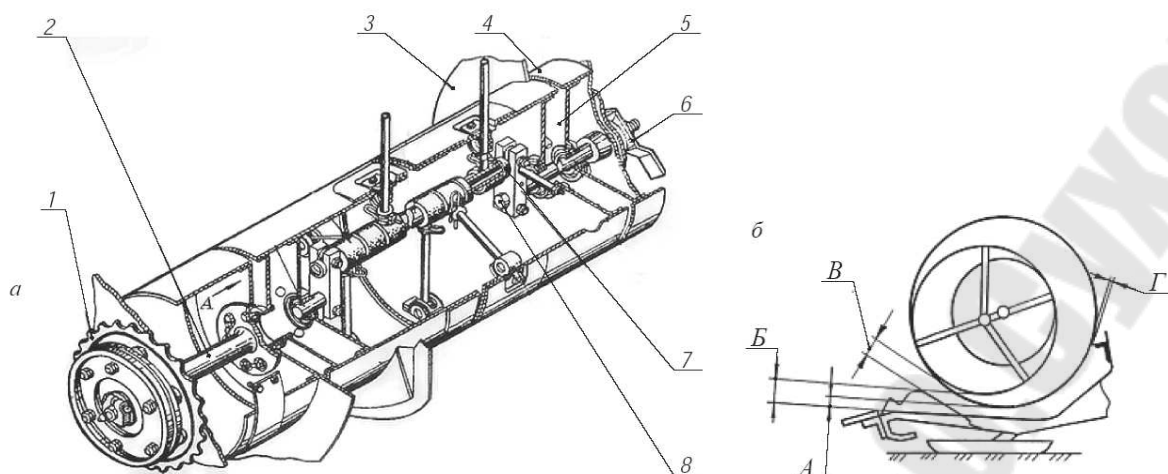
Конструктивная схема и основные регулировки шнека жатки:
